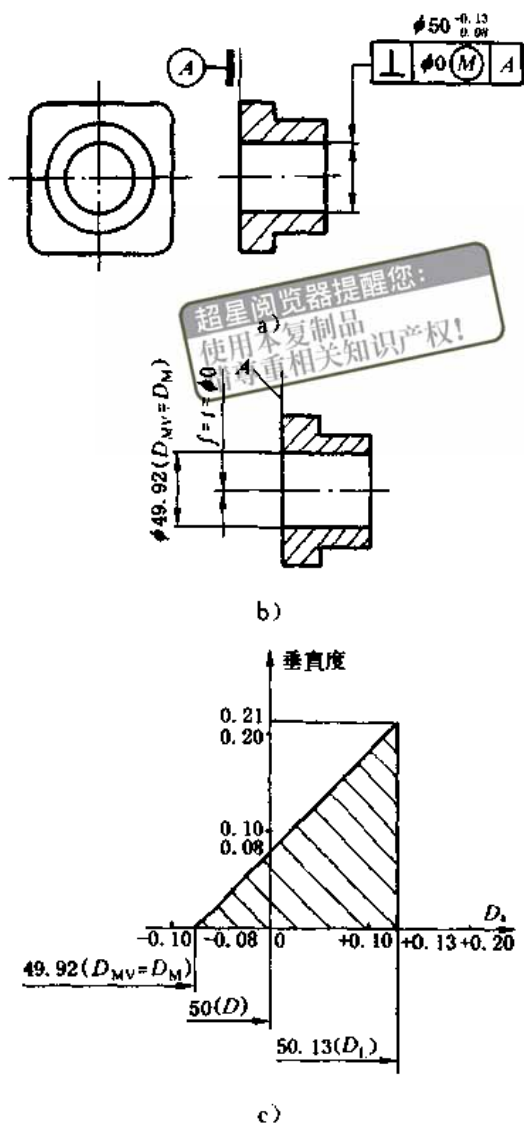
轴线垂直度公差采用最大实体要求的零形位公差
